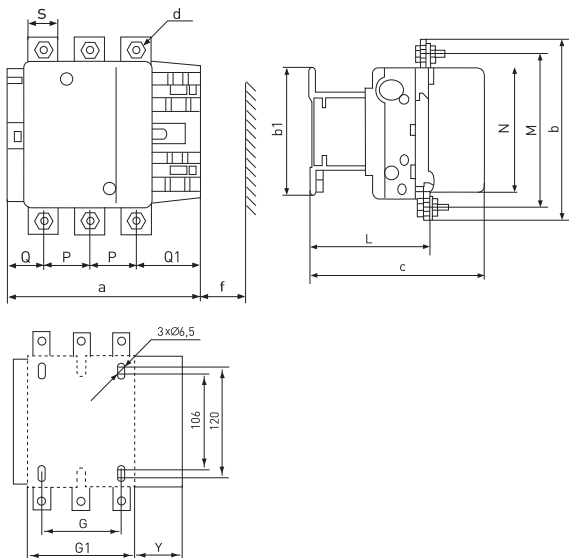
Габаритные и установочные размеры КТЭ-1 (115А; 150А; 185А; 225А; 265А; 330А)
